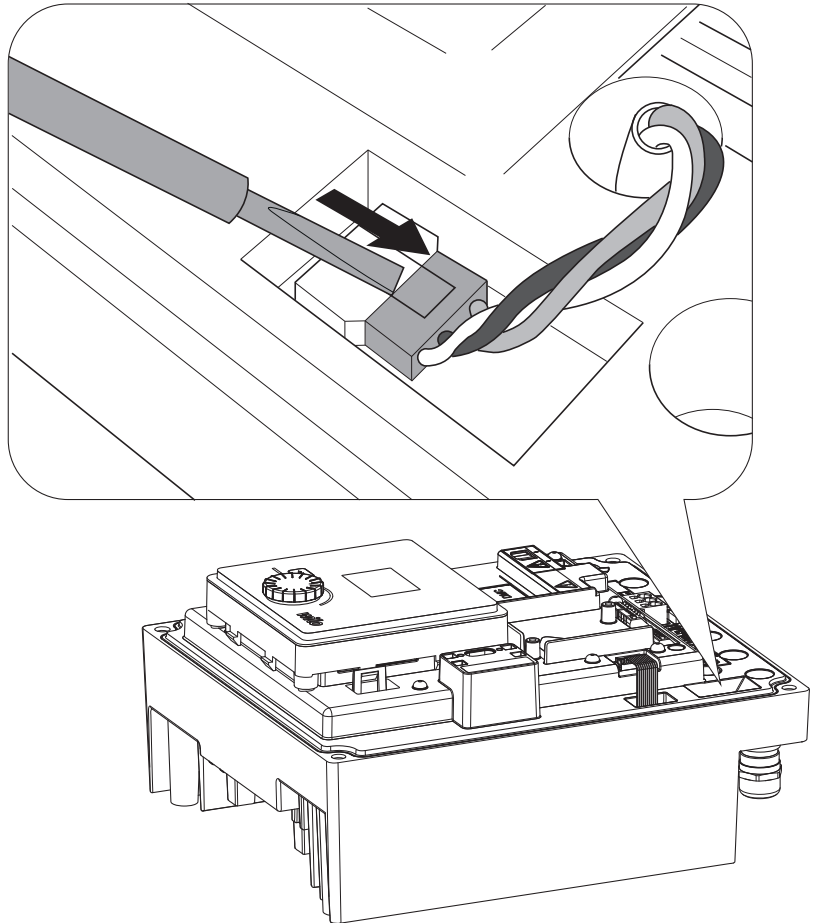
Soltar el cable de conexión del ventilador del módulo
